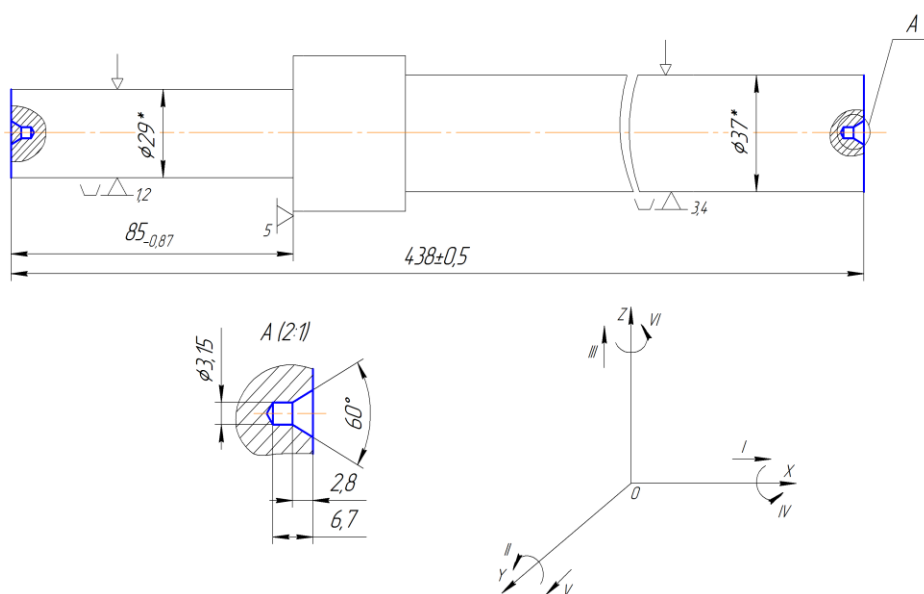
Схема базування деталі для фрезерно-центрувальної операції (варіант 1)
